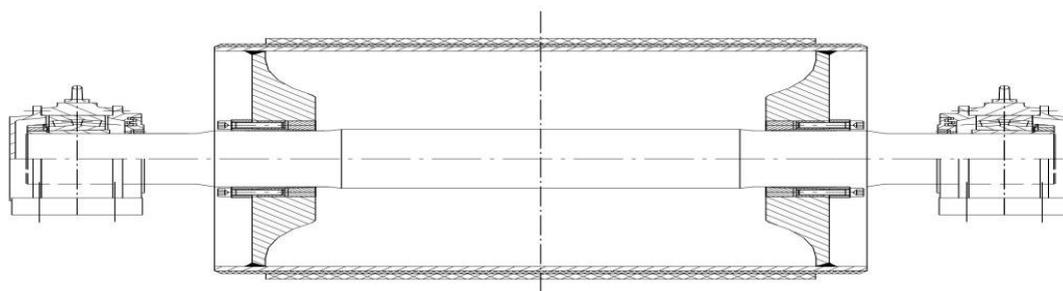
Типовой неуправляемый (без привода) шкив
